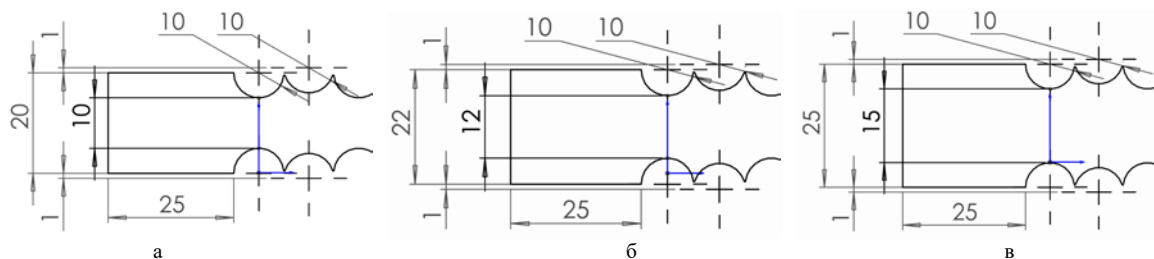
Розташування компактного пучка труб (вигляд зверху):
